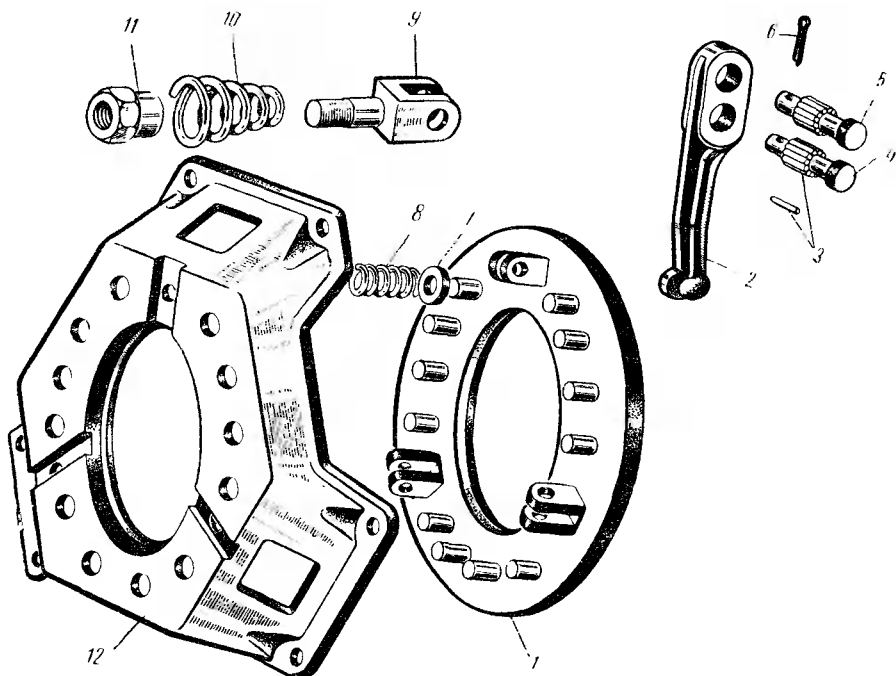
Нажимный диск сцепления двигателя ЗМЗ-53:
